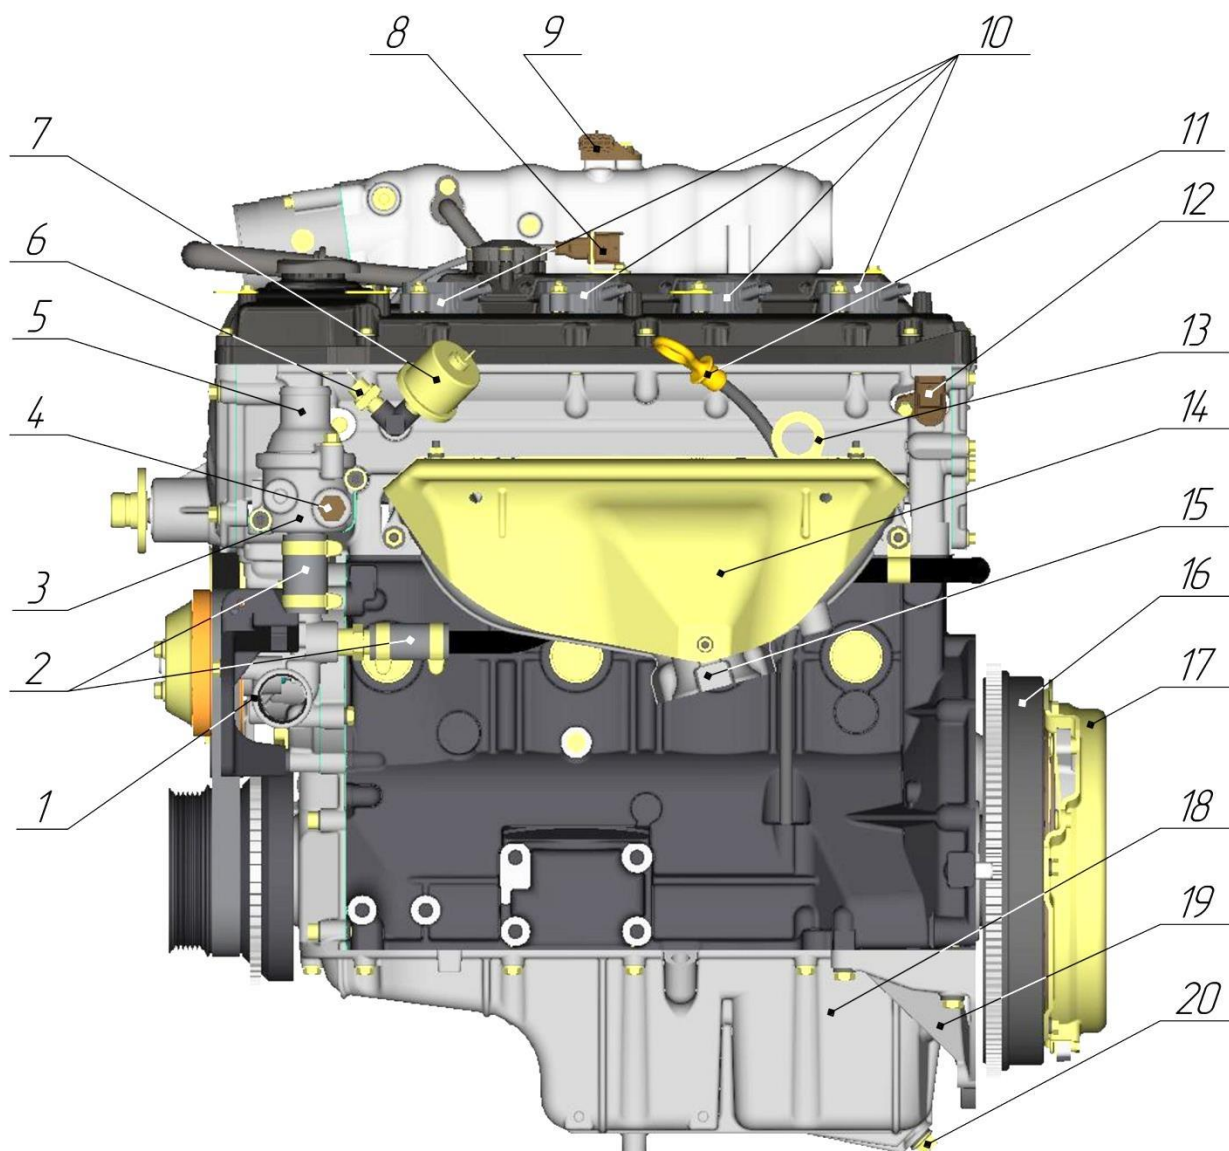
Вид справа двигателя ЗМЗ-40905.10:
